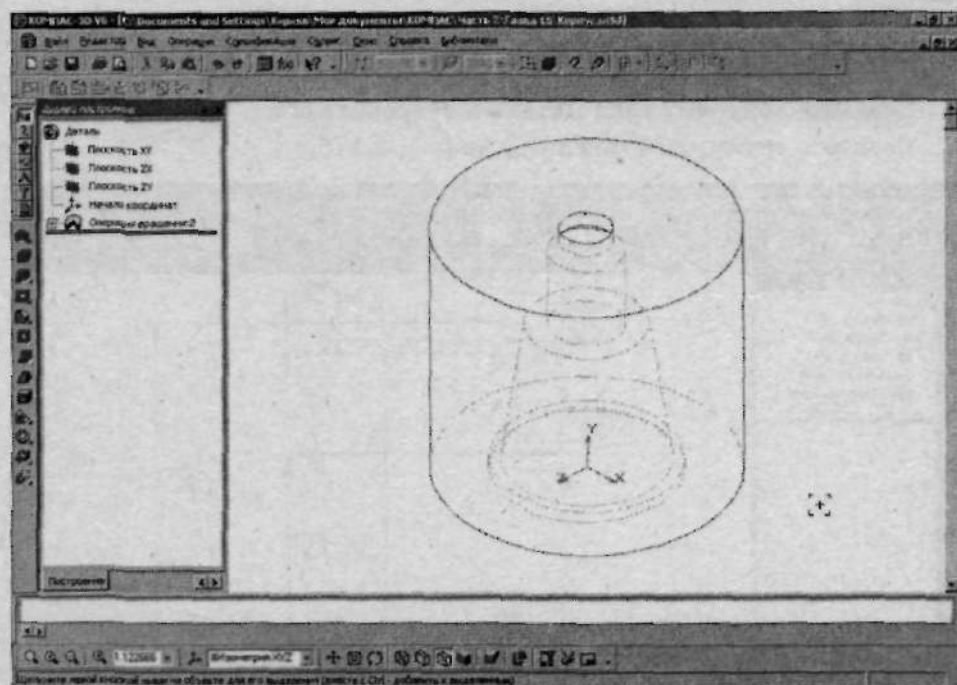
Чтобы создать заготовку для детали, используйте операцию вращения
